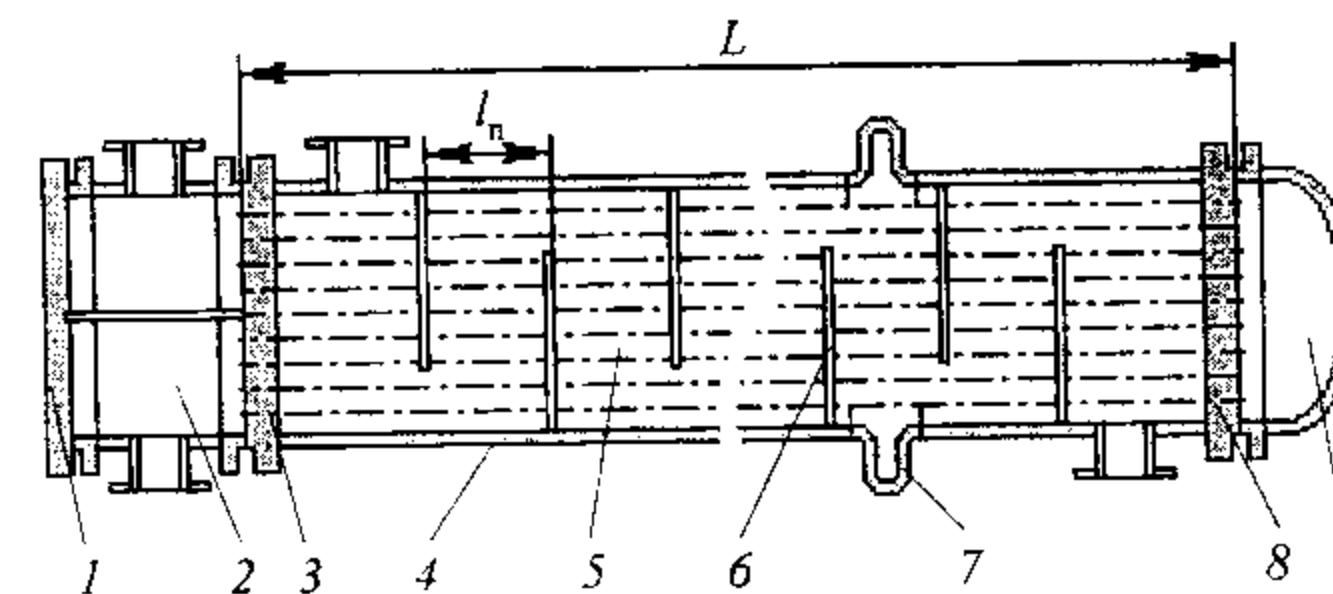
Кожухотрубчатый двухходовой холодильник:
